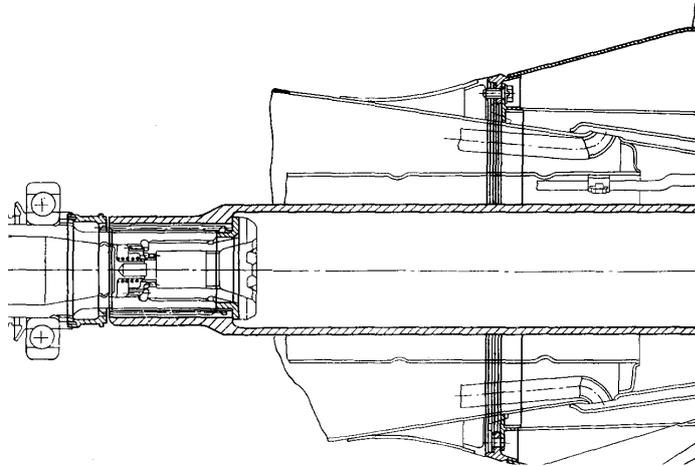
Конструкция разъемного ротора турбины низкого давления турбовинтового двигателя
